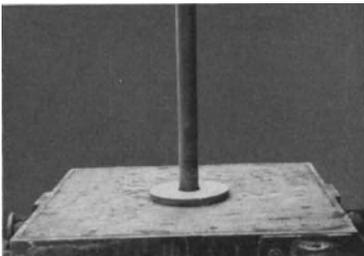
Aufstamppform für den Oberkasten mit über die Spindel geschobener Gippscheibe.
